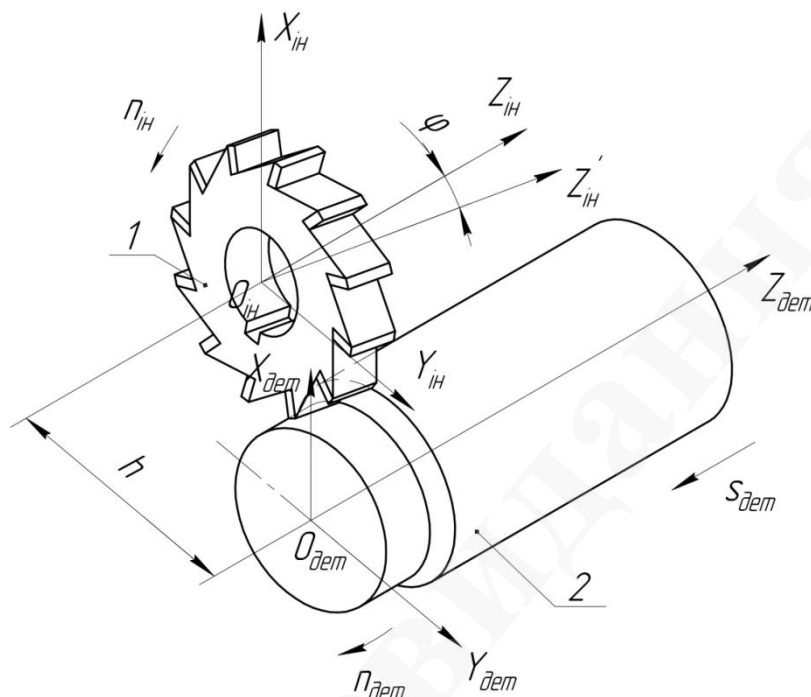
Схема фрезерування циліндричної поверхні орієнтованим інструментом:
